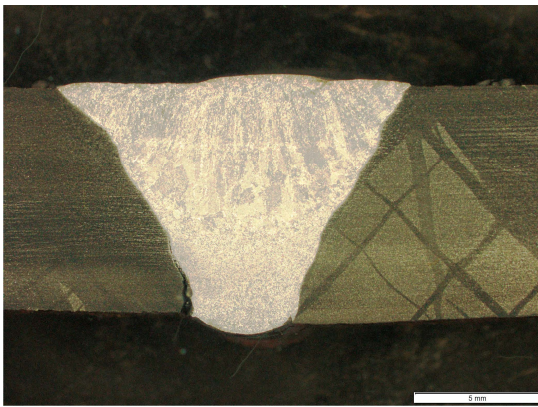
Probe G04-05, Schweißnaht FAT 71, Durchläufer
